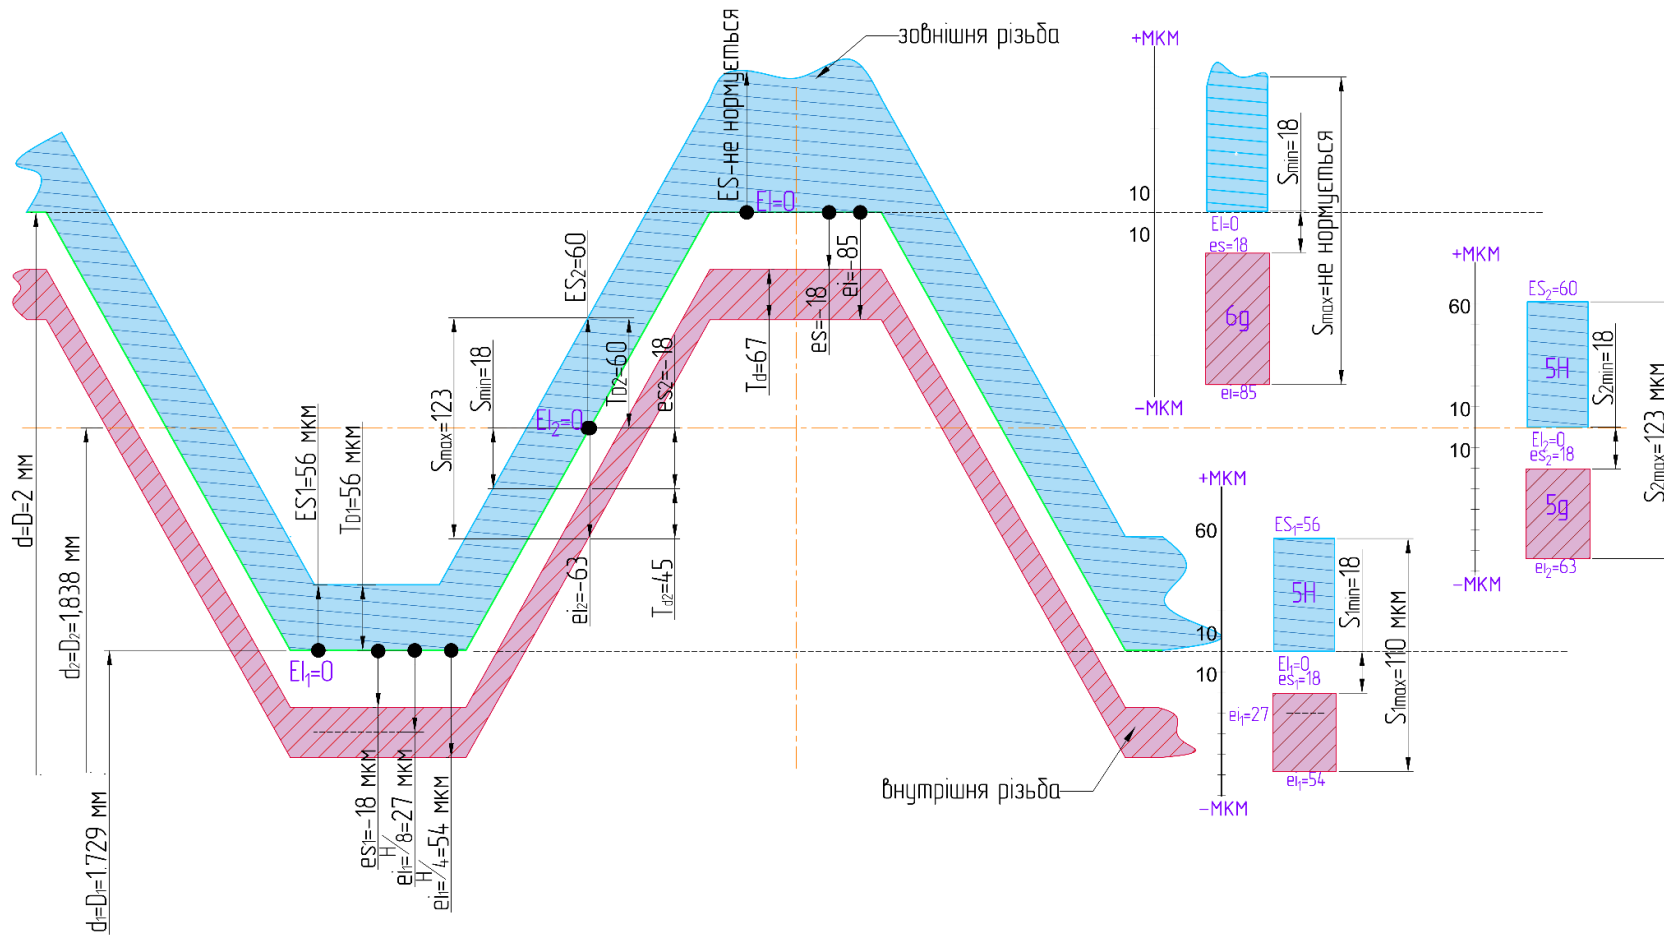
Схема розташування полів допусків за основними діаметрами внутрішньої нарізі $M2 \times 0,25 - \frac{5H}{5g6g}$
